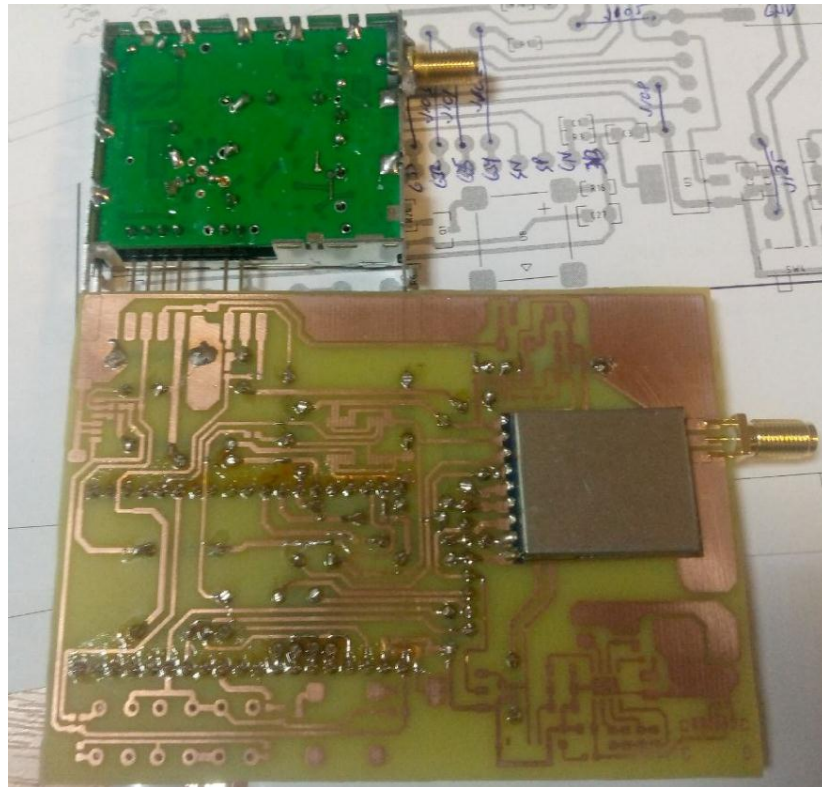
Тестовий зразок плати, виготовлений на фрезерному станку
